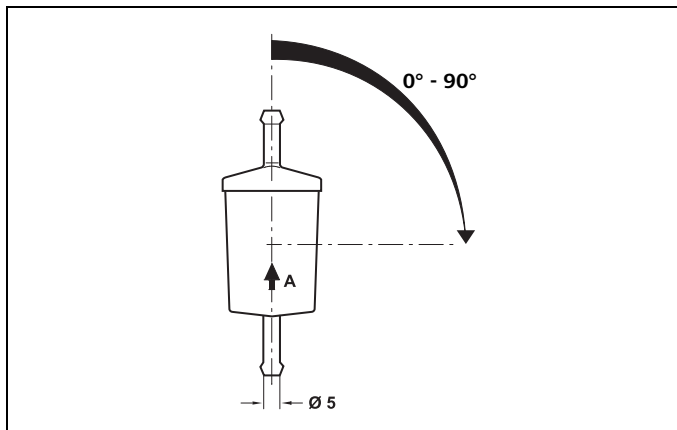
Топливный фильтр, монтажное положение и направление потока
